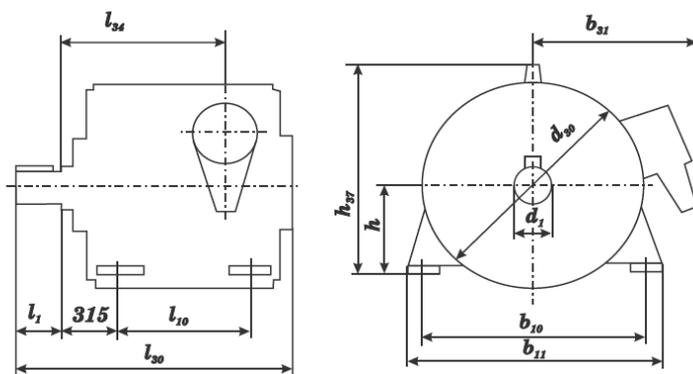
Габаритные, установочные, присоединительные размеры двигателей АКД
